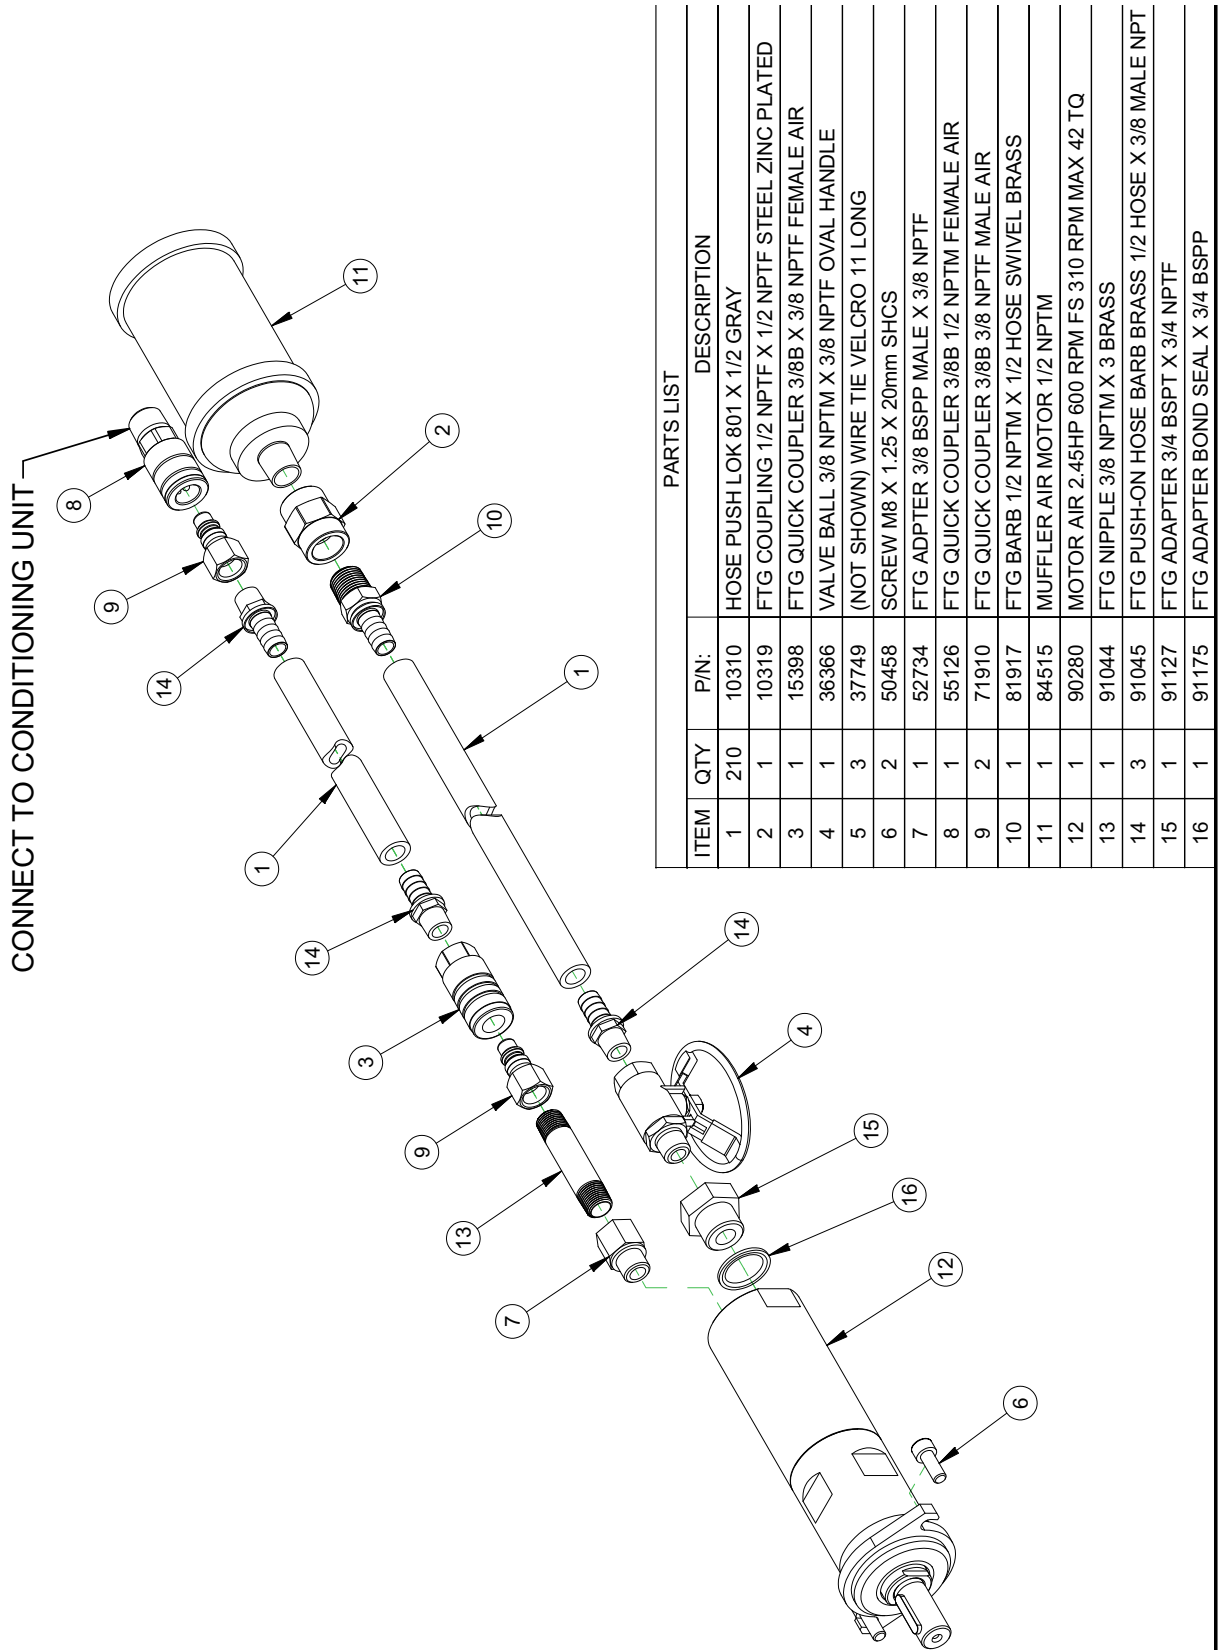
LISTE DES PIÈCES MANDRIN DE LA FF5300, DI (P/N 89990)
